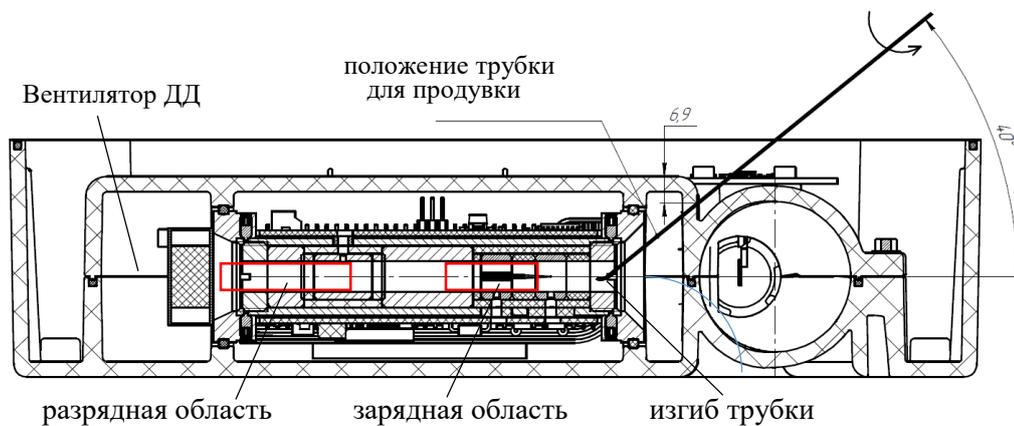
Расположение трубки баллона для продувки датчика дыма
